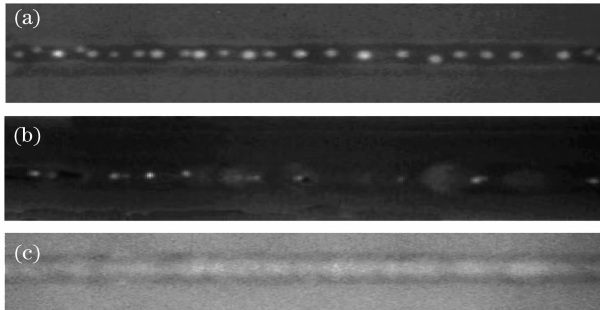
焊接接头X射线图像。(a)激光焊接;
